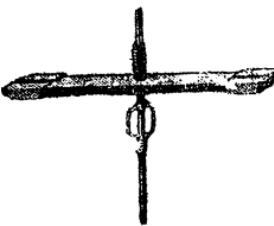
Под якорем прикручивается проволочная рамка прерывателя.
